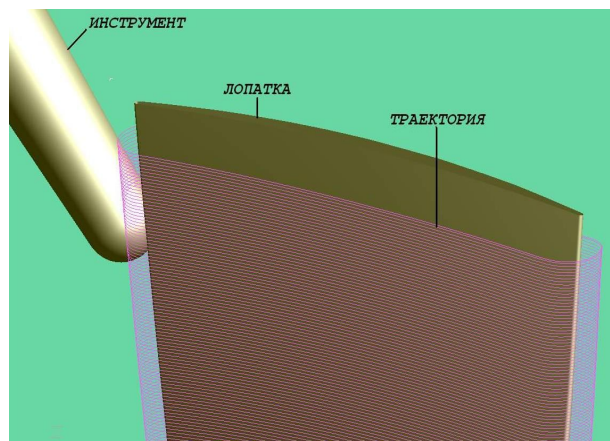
Формообразование пера лопатки моноколеса спиральным высокоскоростным фрезерованием
